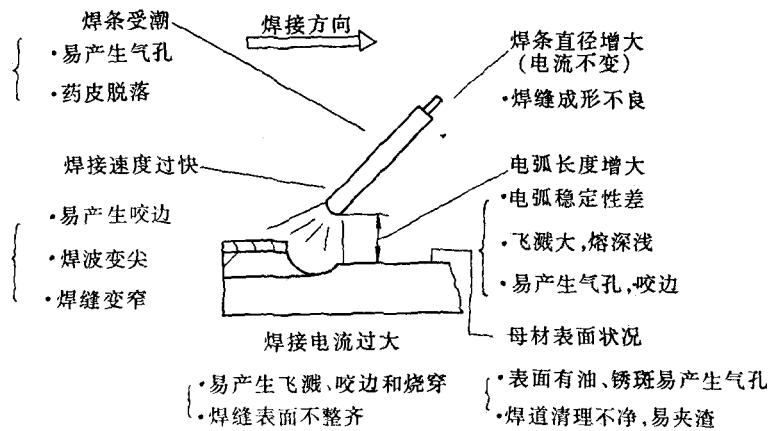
焊接工艺参数影响焊接质量图解
